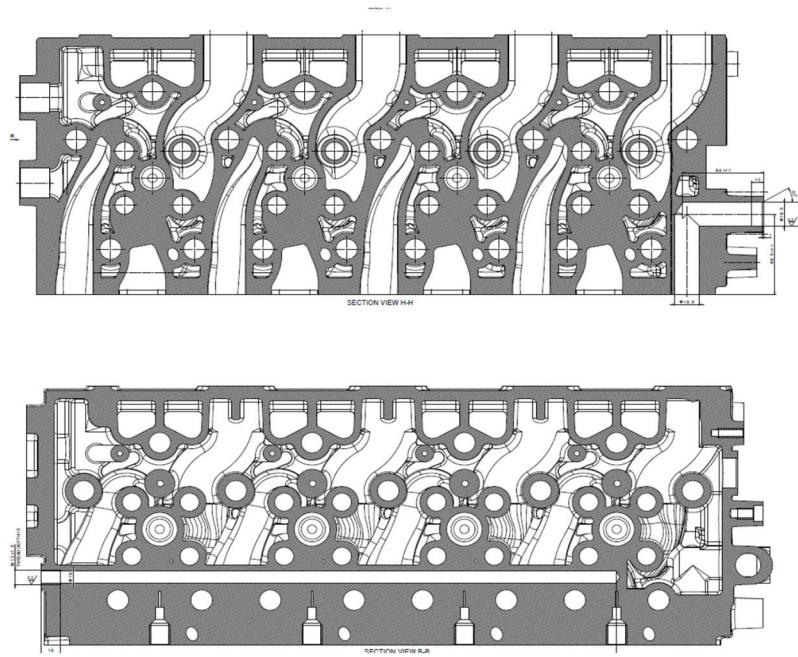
Ortak motor bloğu ile 16 valf silindir kafasının montajı
